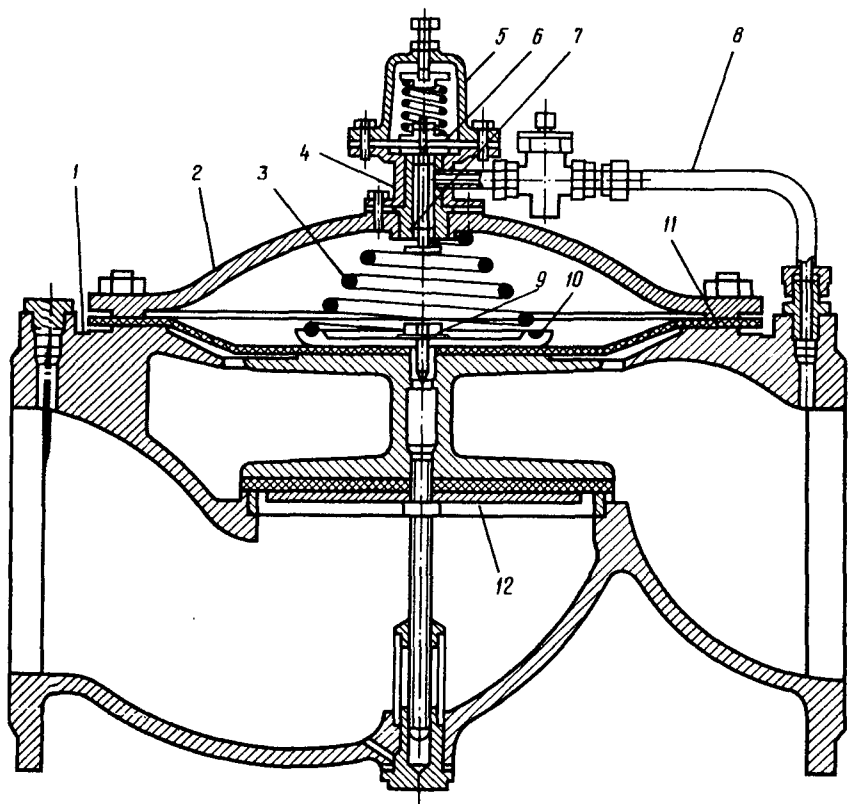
Конструктивная схема регулятора давления РД-1:
